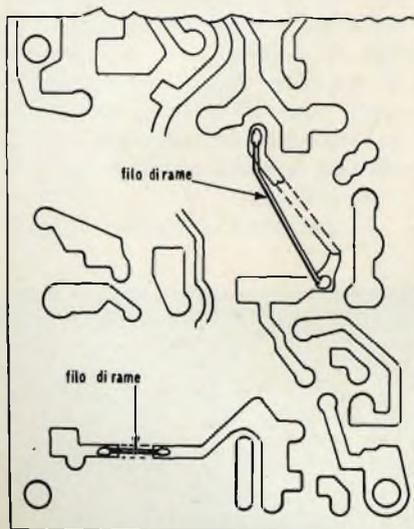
Riparazione di un circuito stampato interrotto mediante saldatura di fili di rame.
